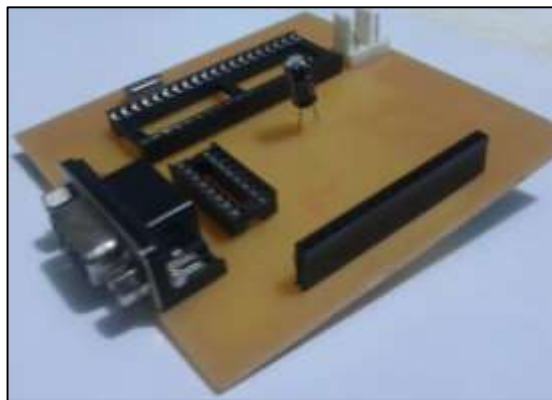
Colocación de los elementos electrónicos en la tarjeta para la soldadura.
